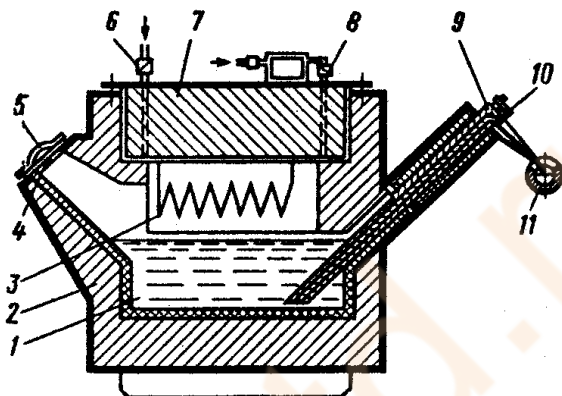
Пневматический дозатор для алюминиевых сплавов:
